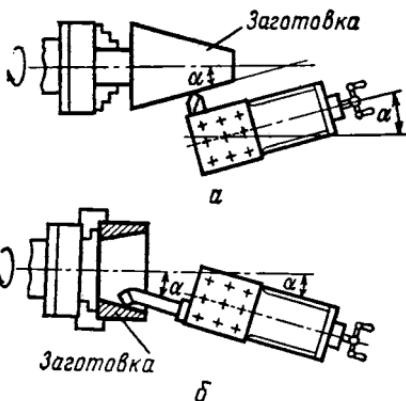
Обработка конической поверхности при повернутых верхних салазках суппорта:
